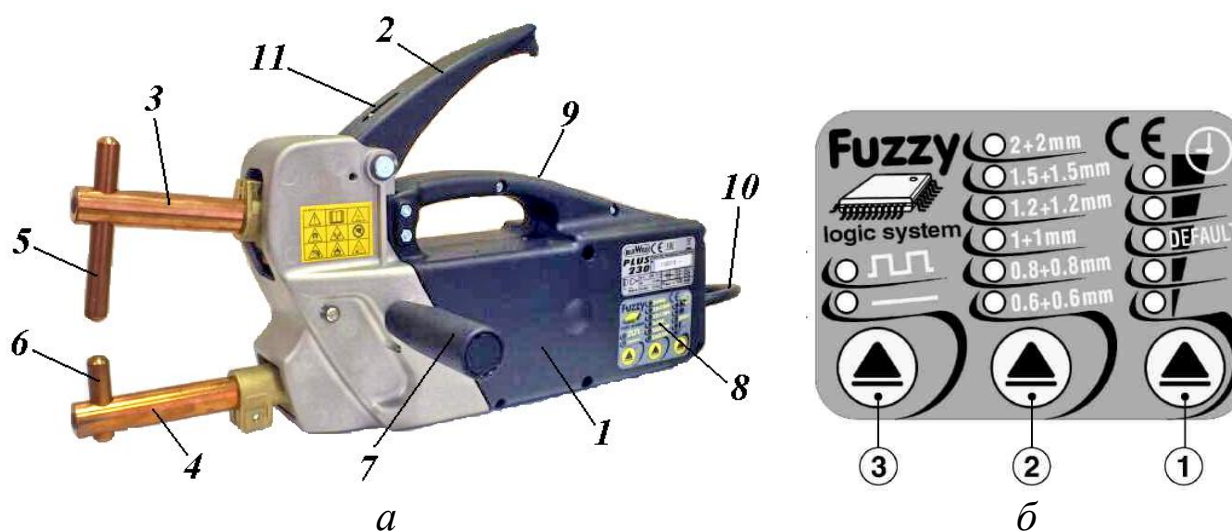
Ручной переносной аппарат Telwin Digital Modular 230: *а* – внешний вид; *б* – органы управления панели настройки режима сварки (обозначения в тексте); *1* – корпус; *2* – рычаг; *3*, *4* – верхний и нижний, соответственно, электрододержатели; *5*, *6* – верхний и нижний, соответственно, электроды; *7* – ручка; *8* – панель настройки режима; *9* – микровыключатель; *10* – кабель питания; *11* – шкала индикатора настройки усилия
